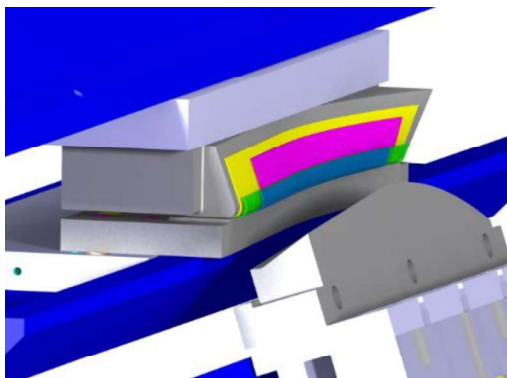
Skalierbare Demonstratoren in einem Werkzeugsatz
